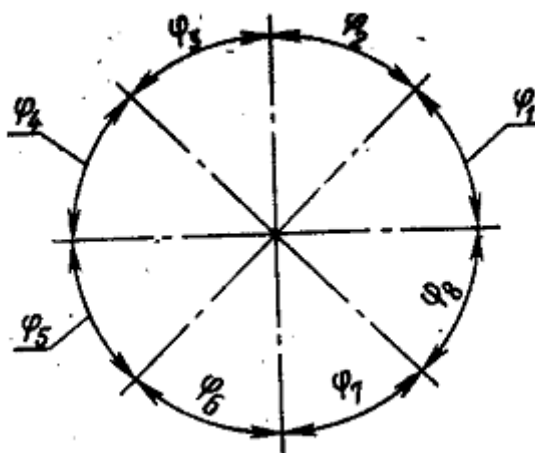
Неравномерность углового шага зубьев фрез
